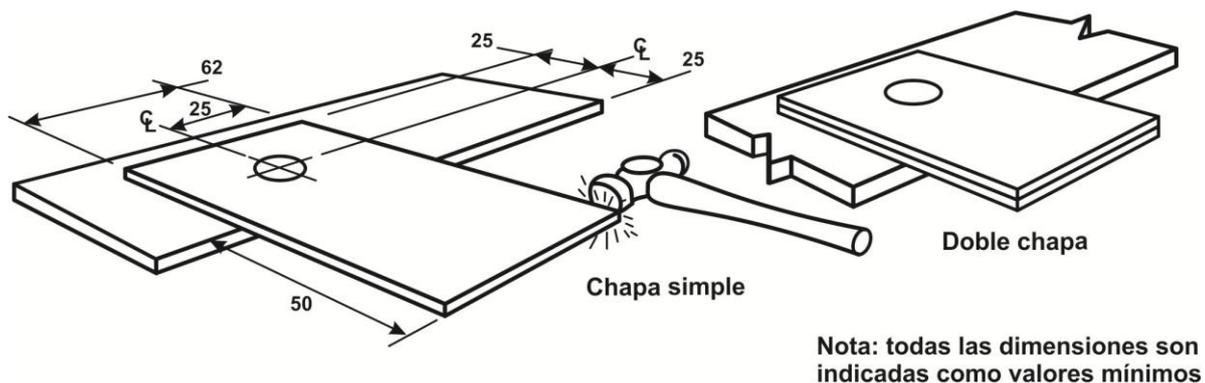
Esquema de ensayo para soldaduras de punto por arco.
